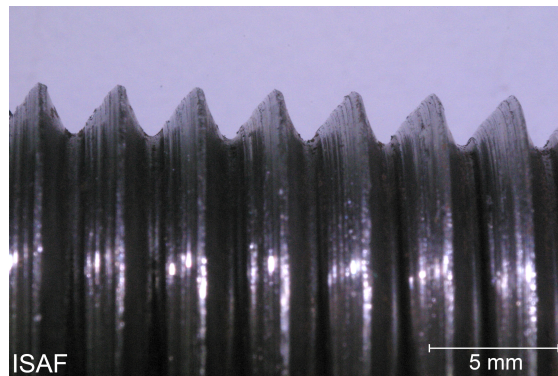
Gewindeprüfkörper axial belastet mit 140kN (Bolzen)
